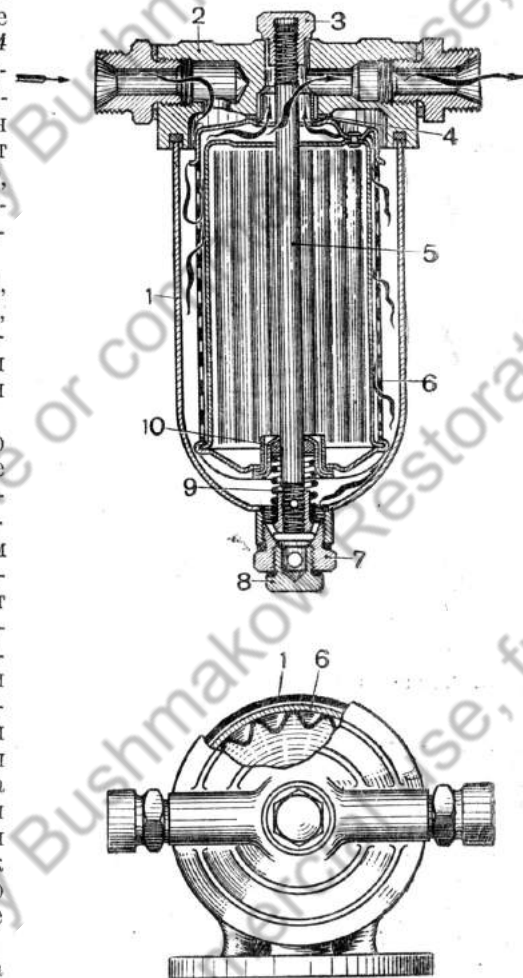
Топливный фильтр грубой очистки: 1 — корпус; 2 — крышка корпуса; 3 — гайка; 4 — прокладка; 5 — шпилька; 6 — фильтрующий элемент; 7 — штуцер; 8 — сливная пробка; 9 — пружина; 10 — сальник
